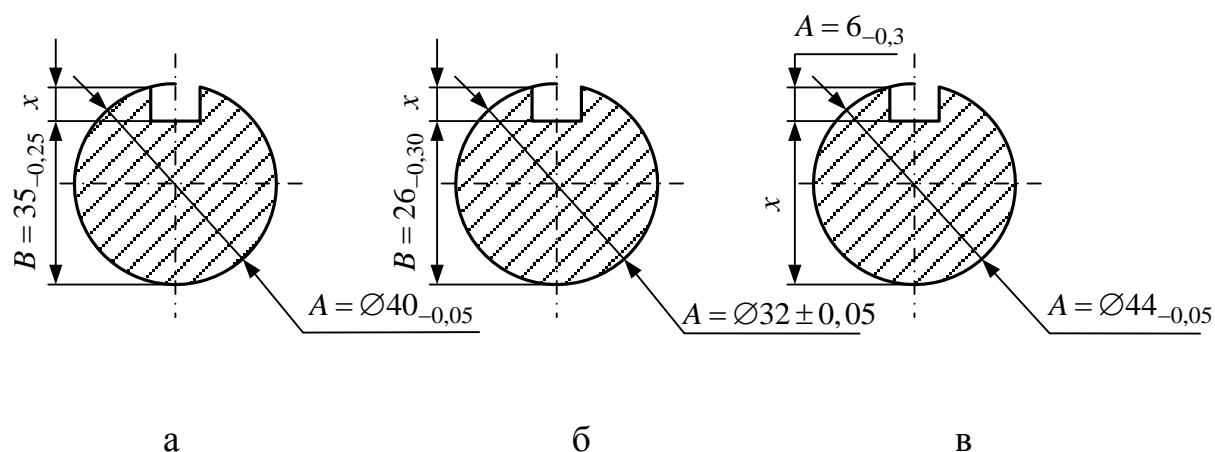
Размеры шпоночного вала по чертежу
